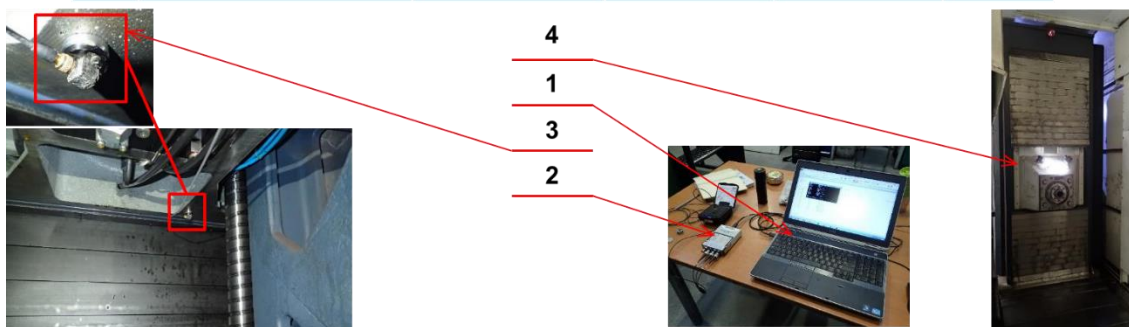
Umístění akcelerometru pod vřeteníkem při zkouškách obráběním
